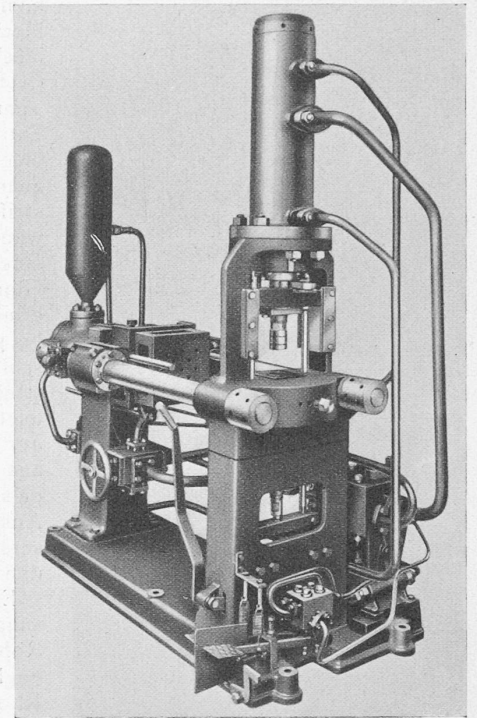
Warmpressgussmaschine Polák. (Der Multiplikator sitzt auf dem grossen Druckzylinder.)
